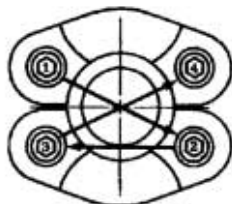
Схема сборки 4-х болтового фланцевого соединения
